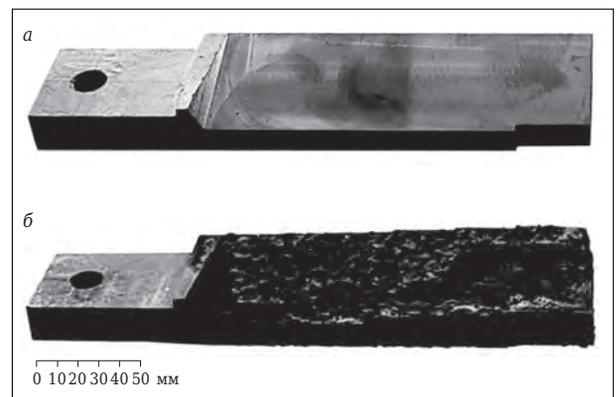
Лопатки смесителя: а — заготовка перед армированием; б — заготовка после армирования пластинами твердого сплава
